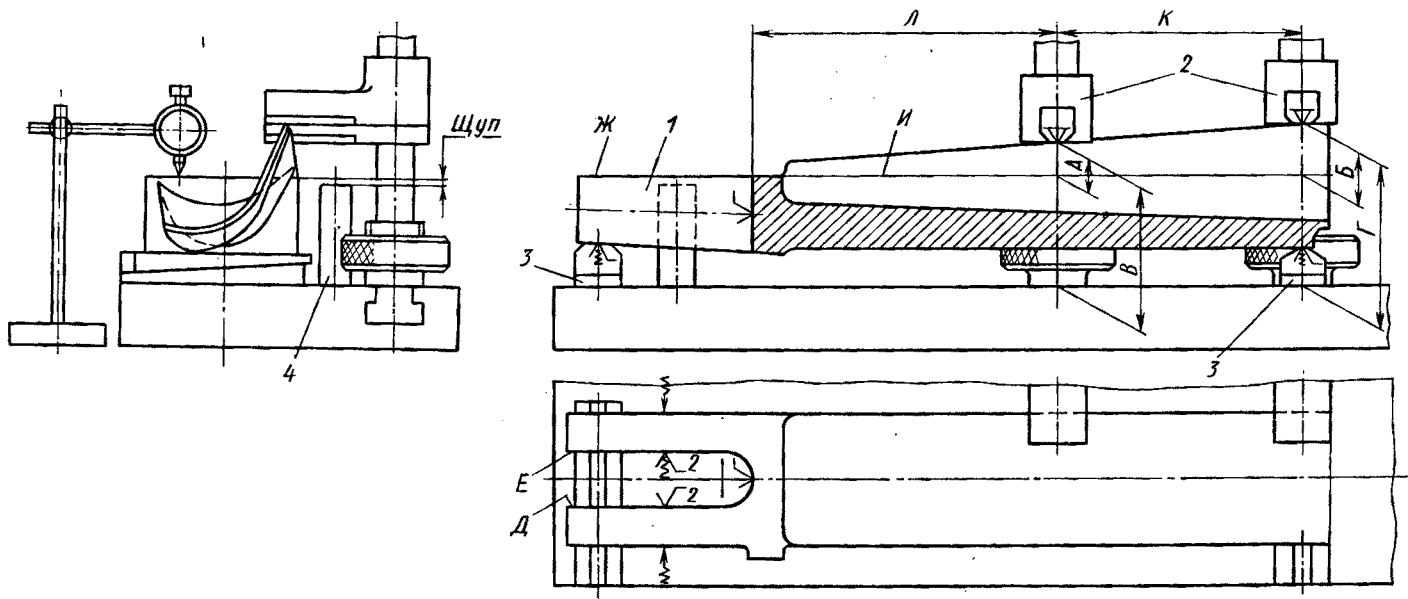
Схема установки для измерения и чистовой обработки радиальных поверхностей хвоста лопатки
